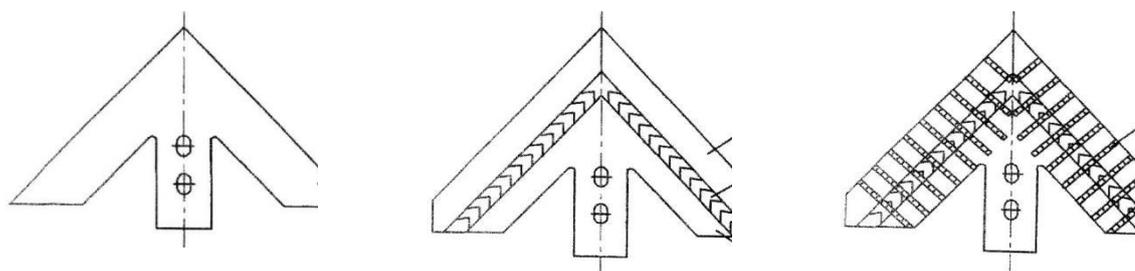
Восстановление и упрочнения культиваторной лапы: 1 - оставшаяся часть детали после эксплуатации; 2 – не изношенная область детали; 3 - компенсирующая вставка; 4 - сварочный шов; 5 - армирующие валики
